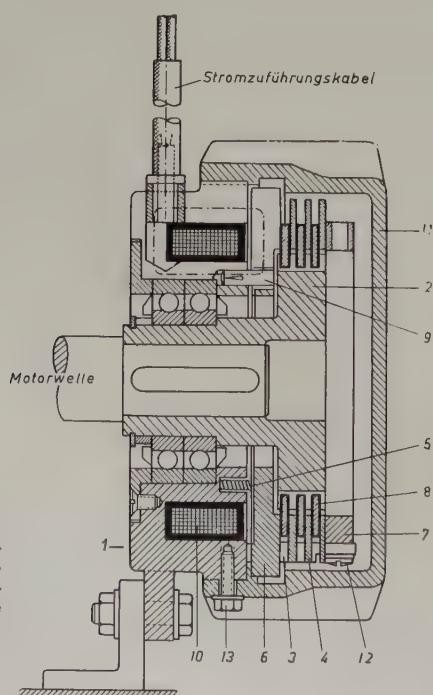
Schnitt durch aufsteckbare Elektromagnet-Lamellen-Federdruckbremse
